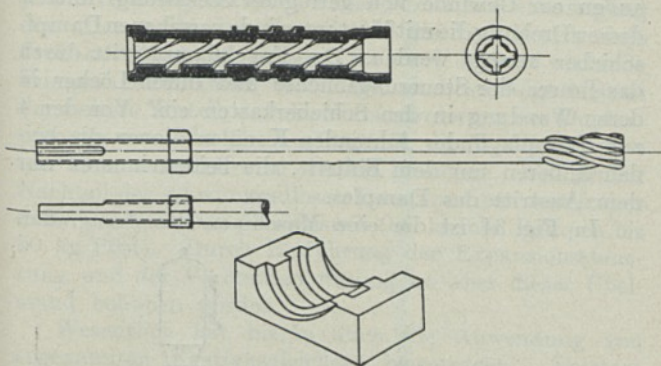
Teile der Steuerung der Patent-„Automat“-Dampfmaschine.
